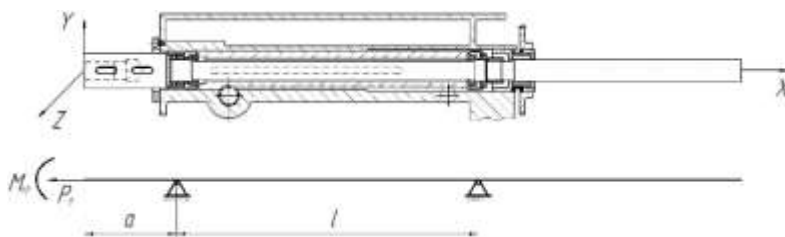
Розрахункова схема шпинделя радіально-свердлильного верстата
